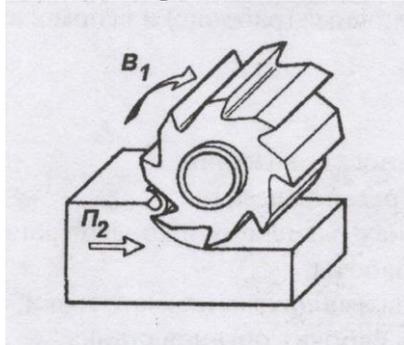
Схема фрезерования призматической заготовки цилиндрической фрезой: V_1 – главное движение – вращение фрезы; P_2 – продольная подача заготовки
